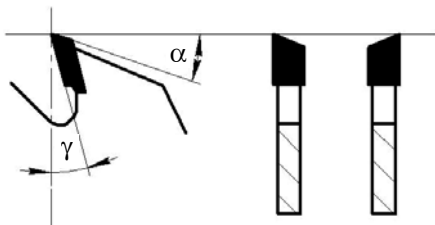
Попеременно косой профиль зубьев дисковых пил с пластинами твердого сплава для распиловки ламинированных ДСтП
